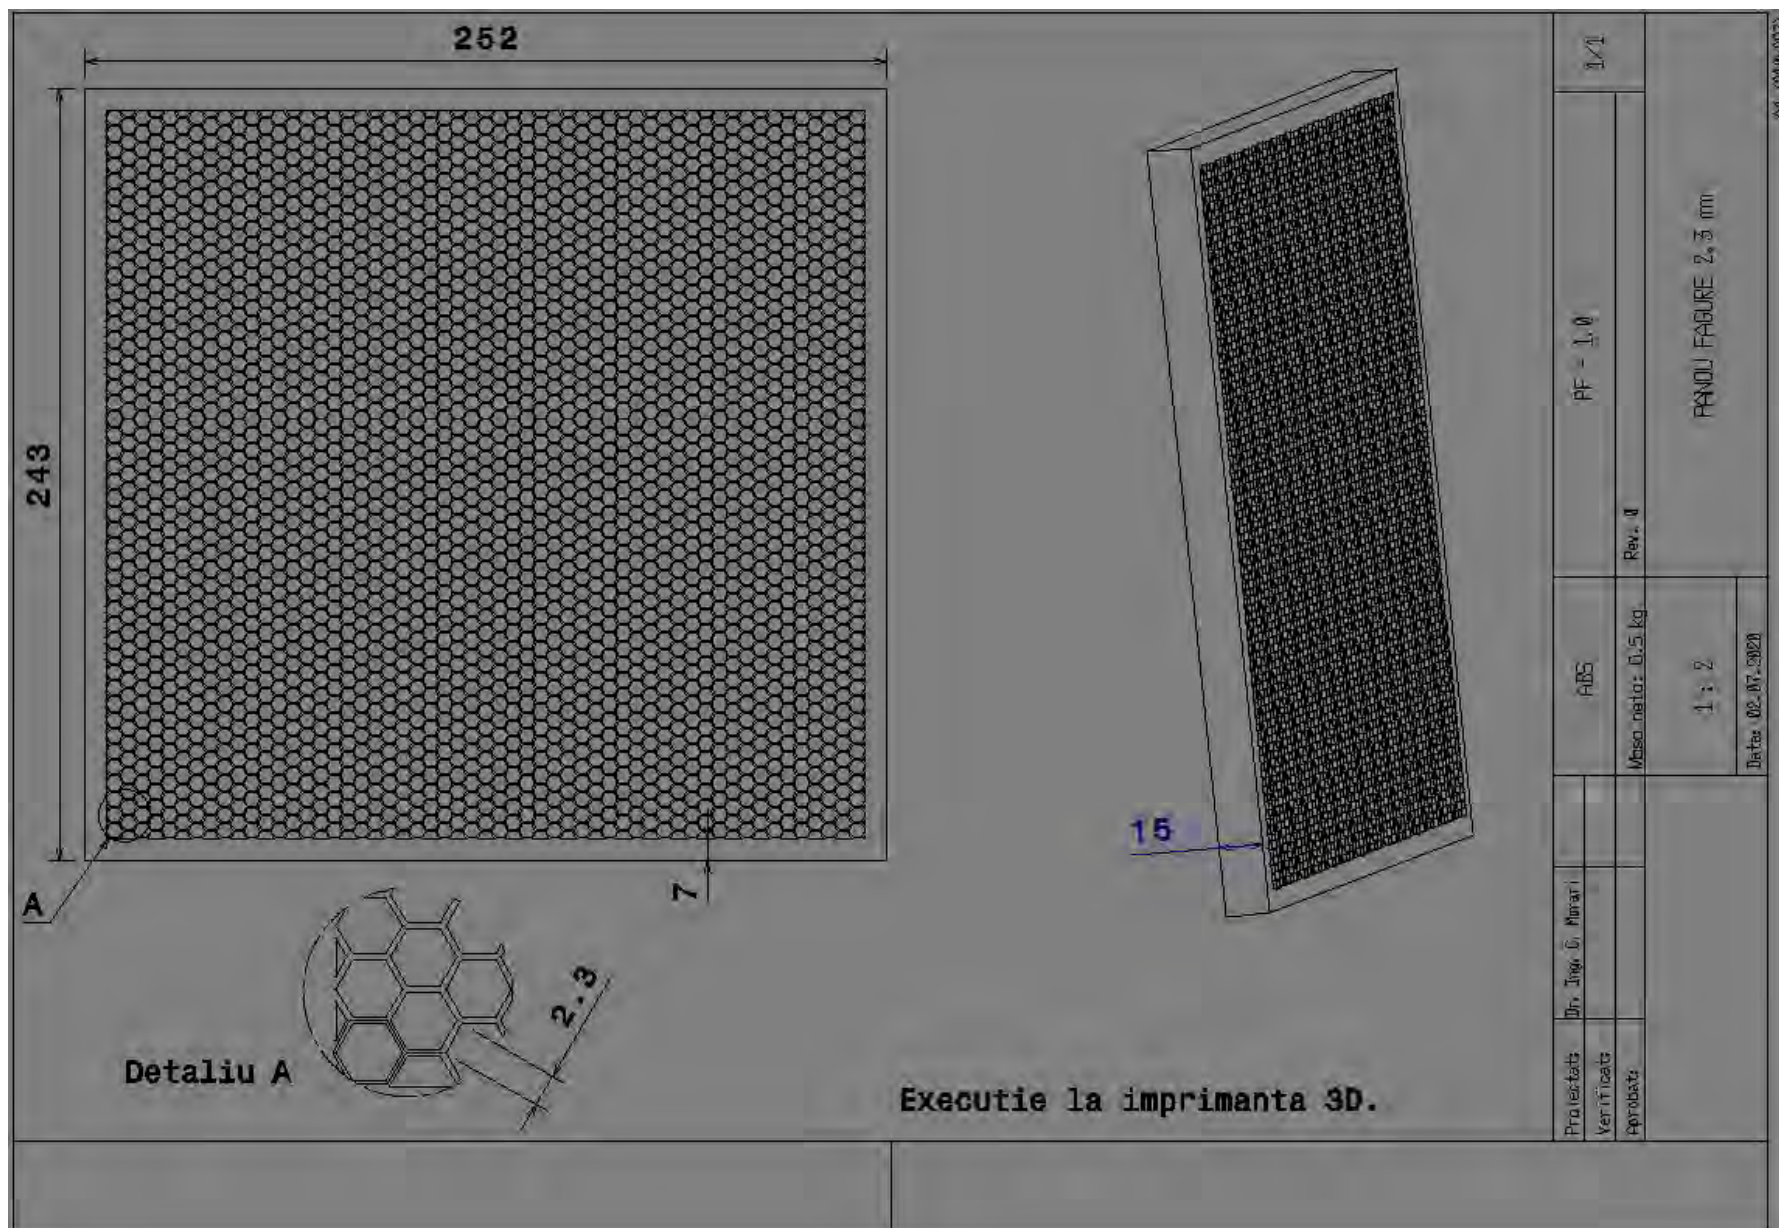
Desenul de execuție al modelului de panou fagure cu perforații hexagonale
